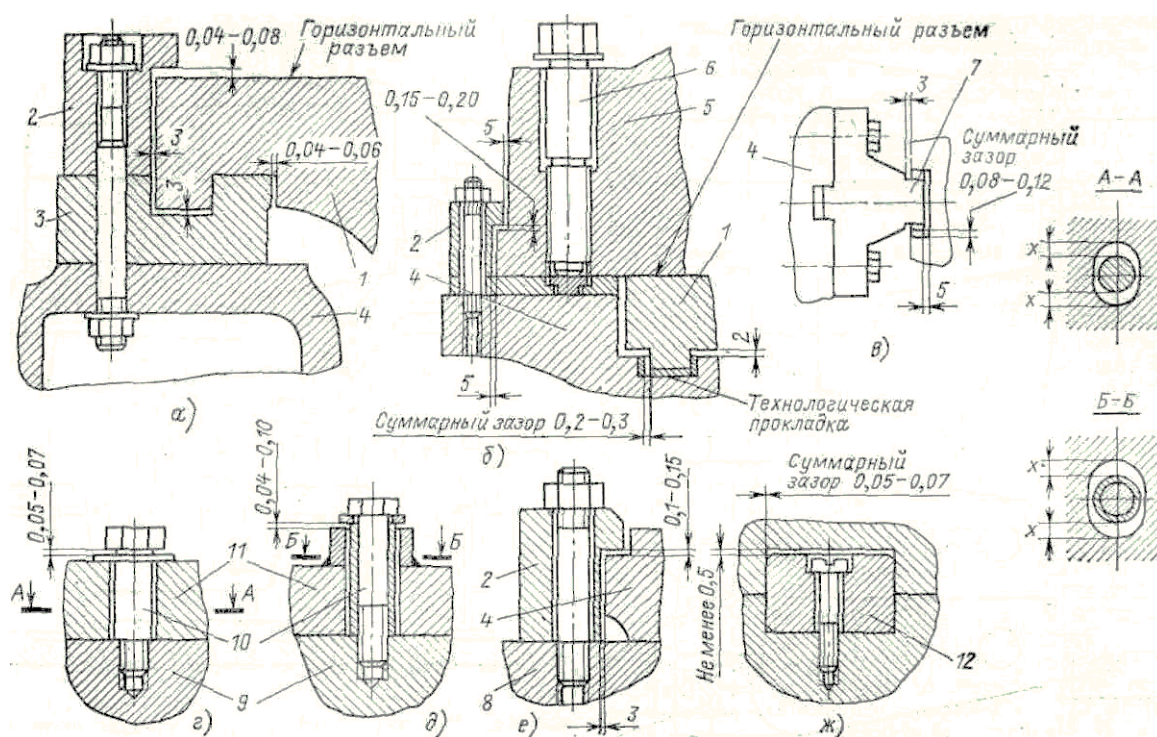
8. Детали крепления корпусов паровых турбин.
